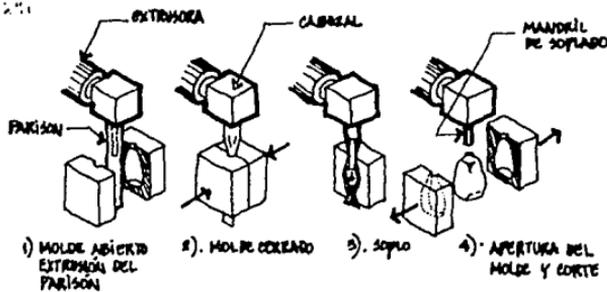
Esquema del proceso de moldeo por Extrusión-Soplo
